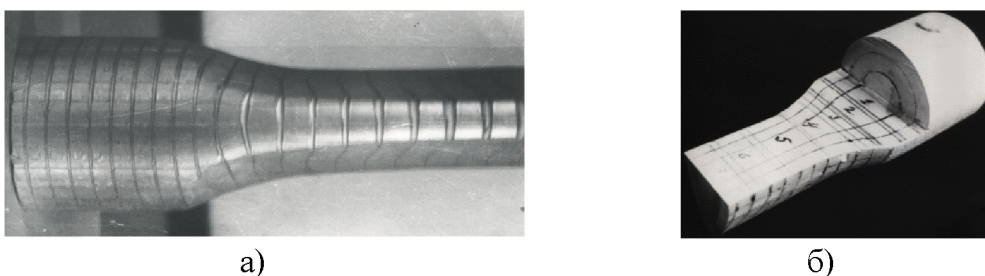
Вигляд координатної сітки на поверхні: а – суцільної; б – складної вальцьованої заготовка зі зразків різних діаметрів:
